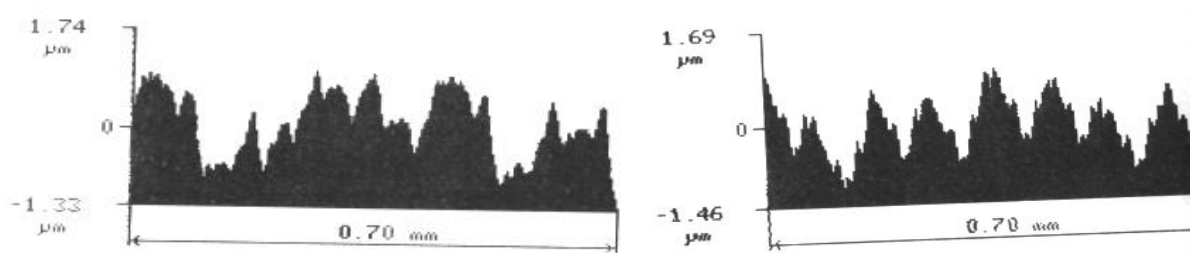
Шероховатость образующей исходного прутка (слева) и поковки (справа)
